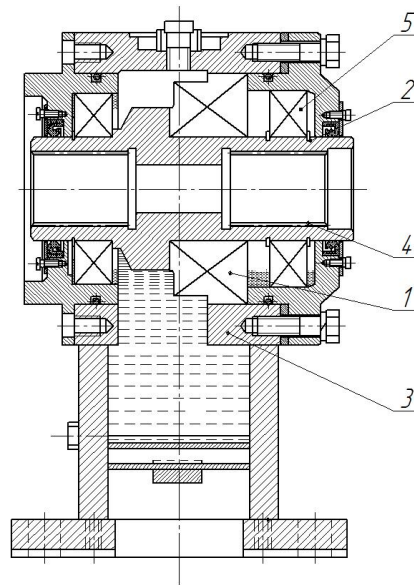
Конструкція вузла опорного підшипника в окремому корпусі:
